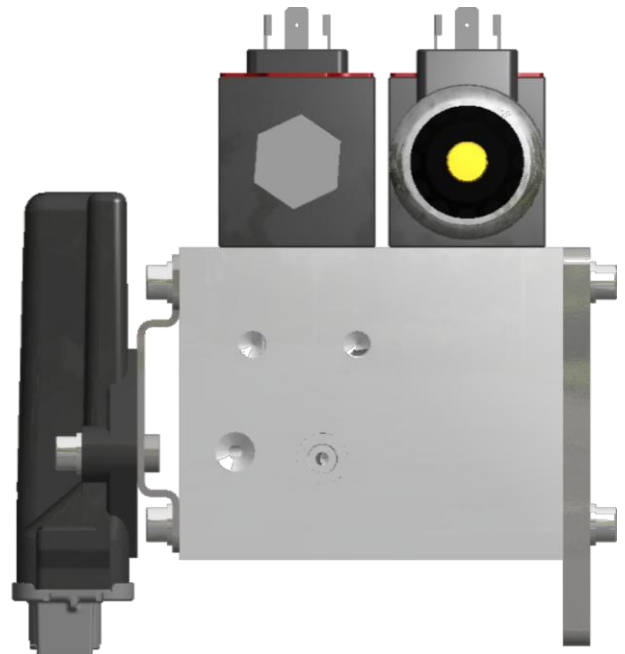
Seitenansicht des am Manifold befestigten Steering Controller.
